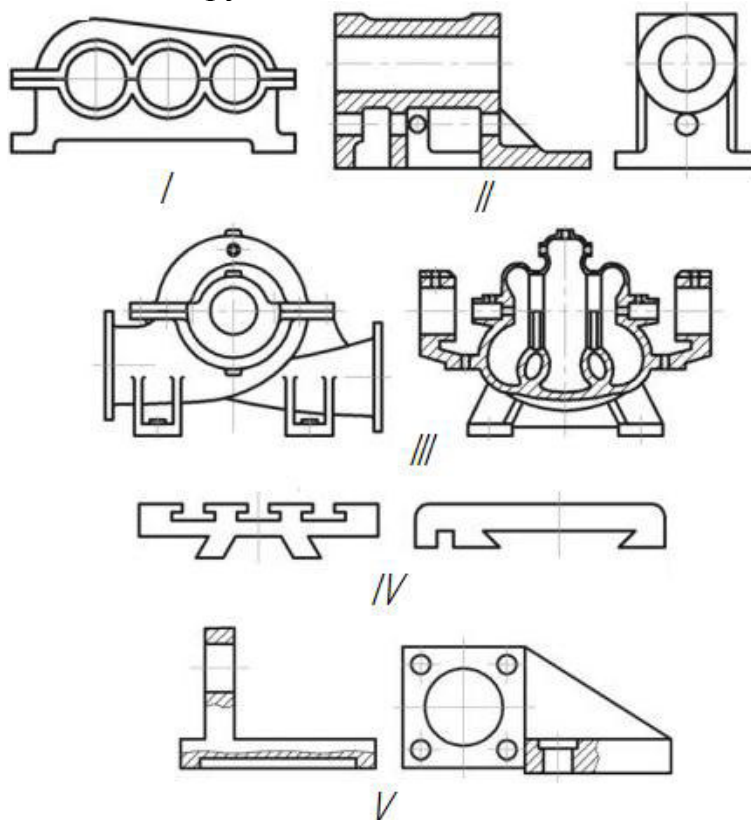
Группы типовых деталей "Корпус" и "Крышка"
